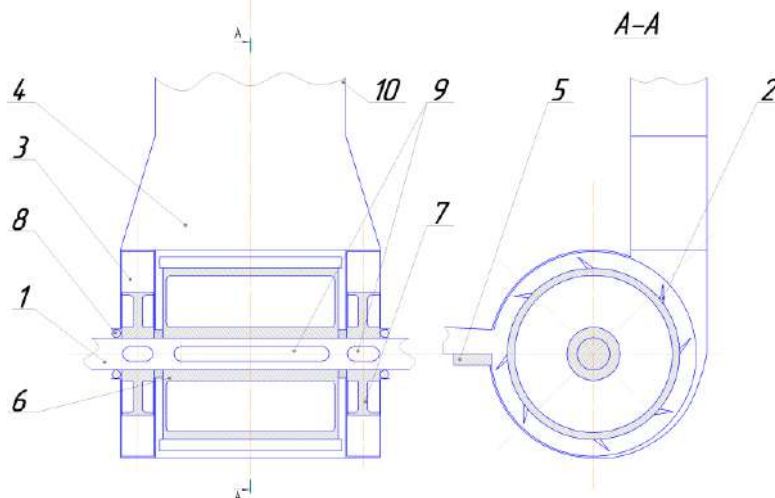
Конструктивні схеми робочих коліс пневматичного транспортера
